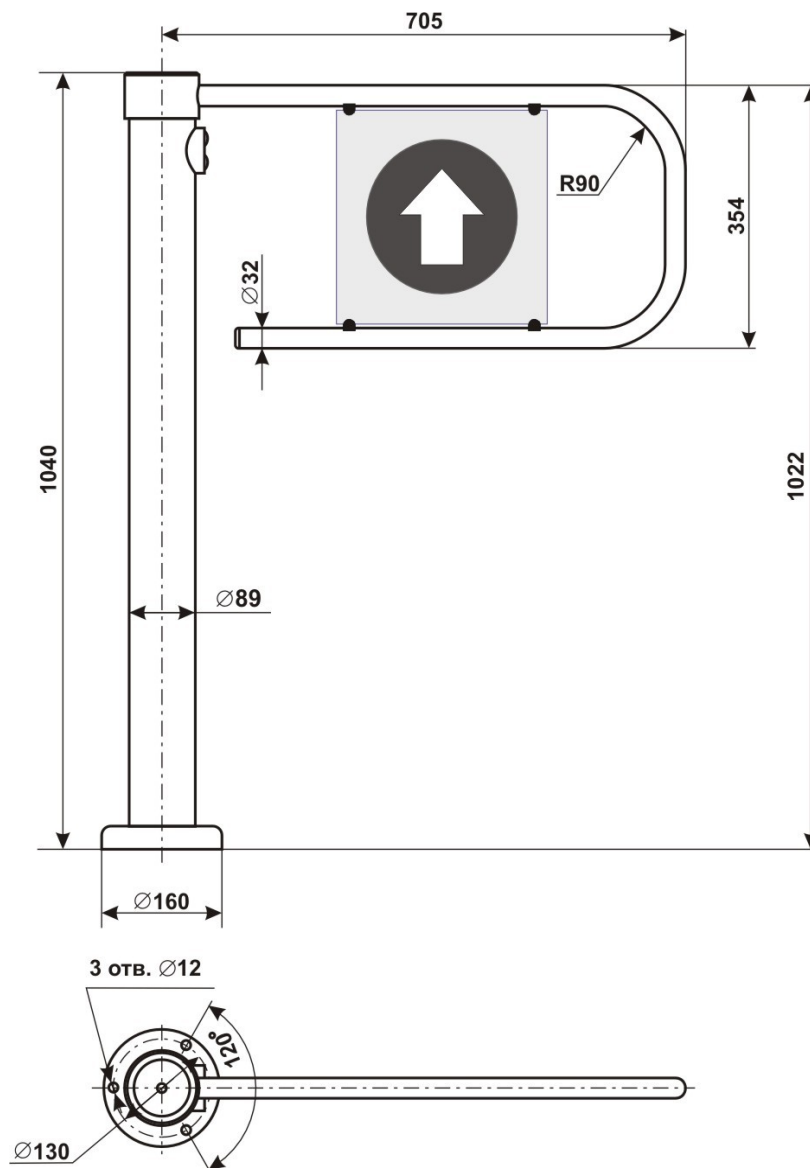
Габаритные размеры калитки PERCo-WHD-04
